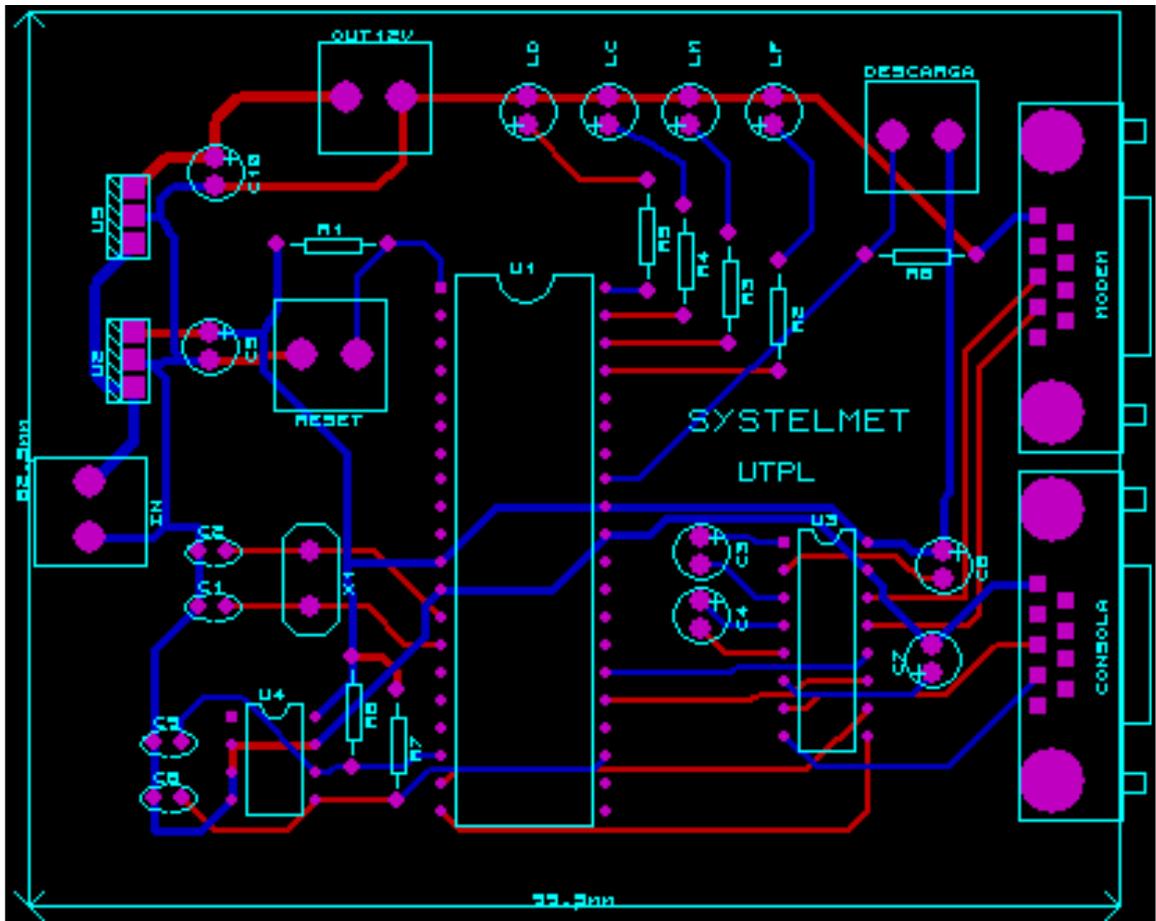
PCB de la tarjeta de adquisición de datos.
